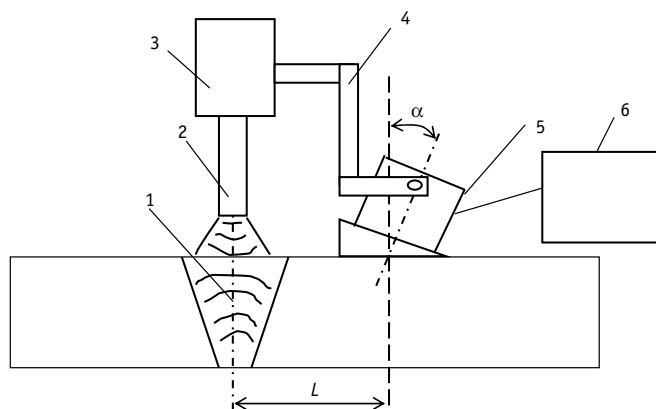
Функциональная схема устройства воздействия ультразвука на околосварную зону в процессе сварки: 1 – сварной шов; 2 – электрод; 3 – держатель; 4 – кронштейн; 5 – ультразвуковой излучатель; 6 – ультразвуковой генератор
